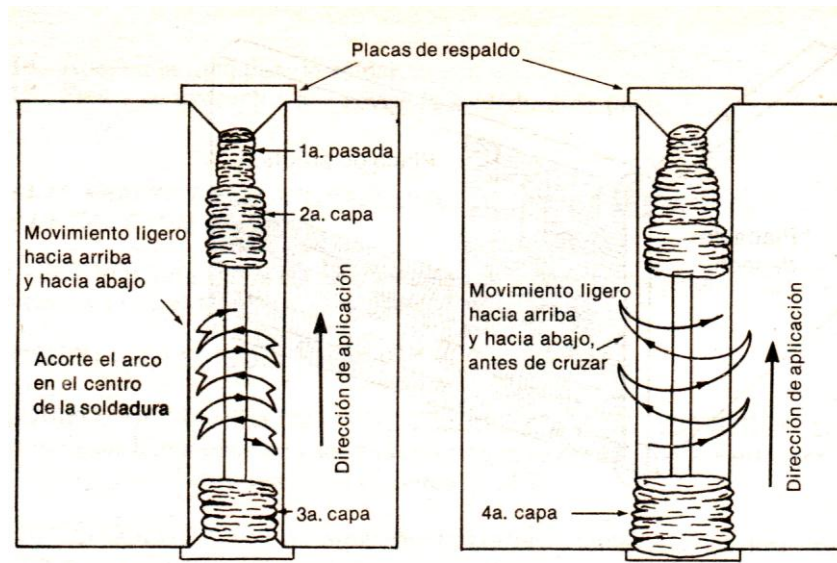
Aplicación de los cordones de soldadura con movimiento oscilante.
